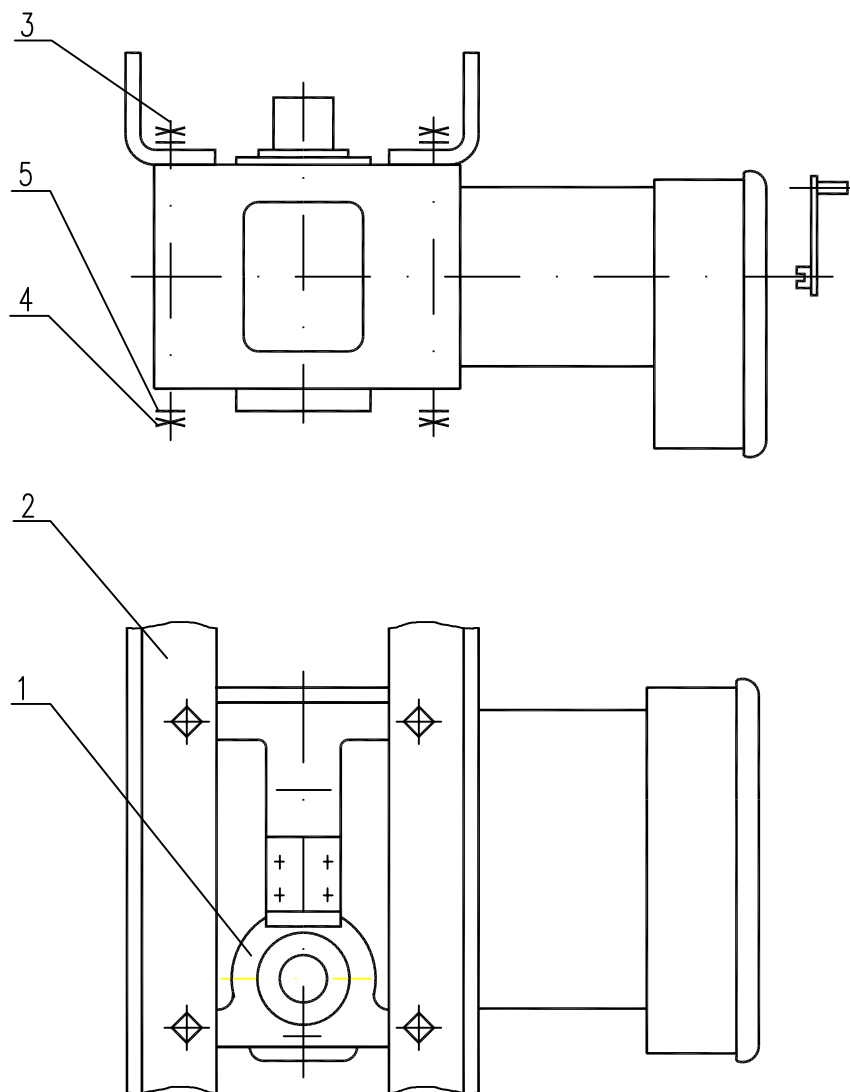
Крепление блока исполнительных приводов типоразмеров ПД-00-01-5УХЛ1 к свае с вертикальным вверх расположением выходного вала. Аналогичное крепление допускают блоки исполнительные приводов типоразмеров ПД-02-08-5УХЛ1, ПД-21-26-5УХЛ1
